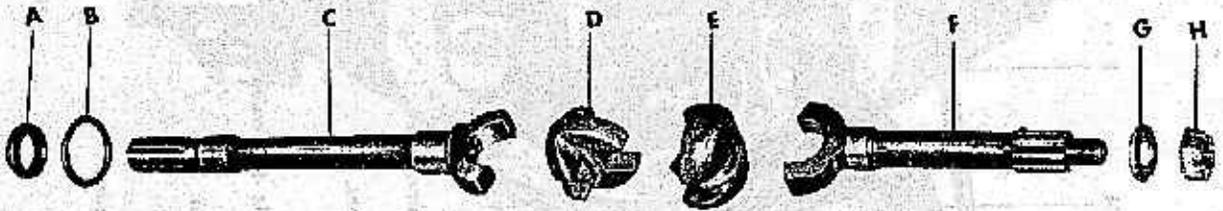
Demi-arbre avant. Vue détalée (joint de cardan type TRACTA)
